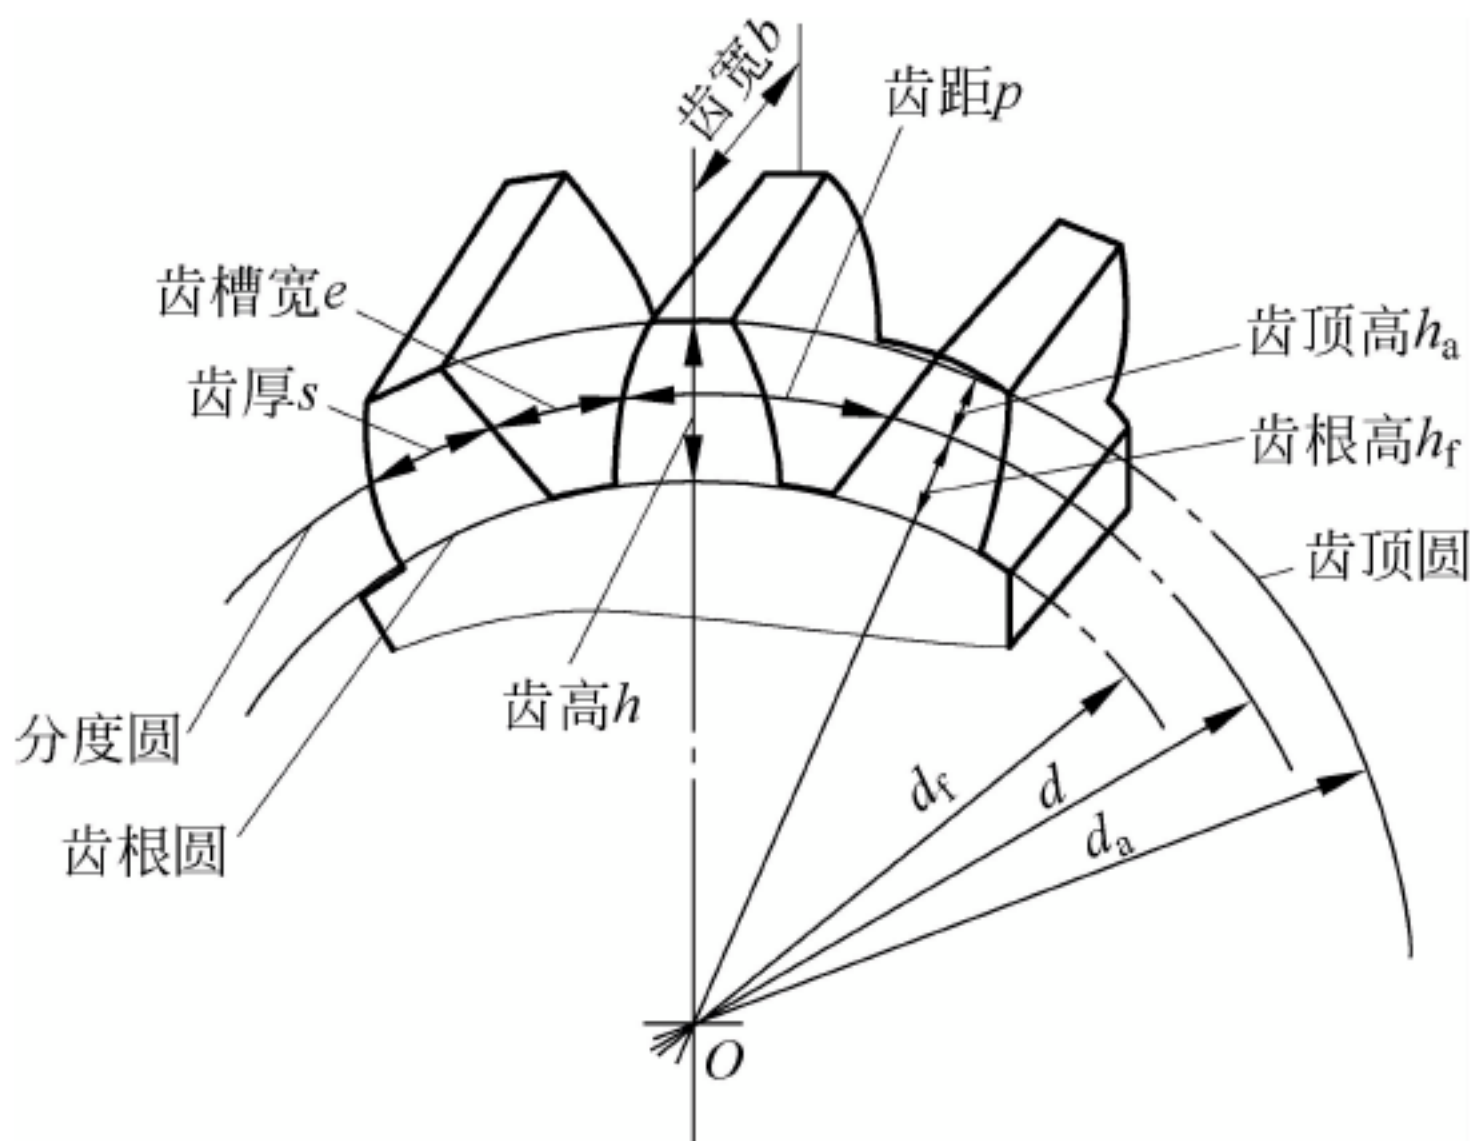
渐开线直齿圆柱外齿轮各部分名称
